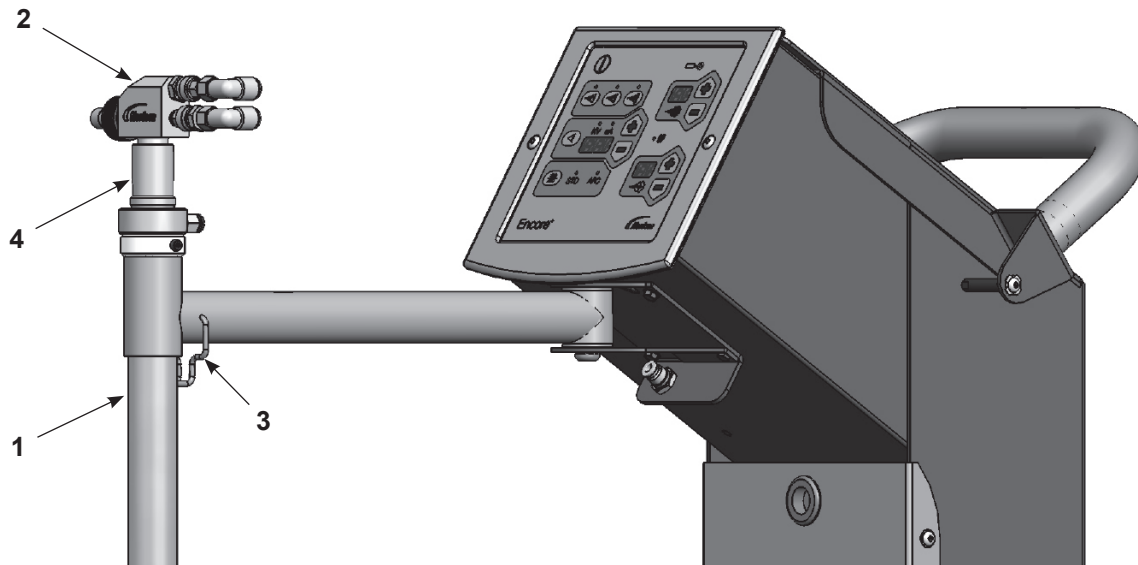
Instalación de la bomba y el tubo de aspiración de pistola Encore LT
